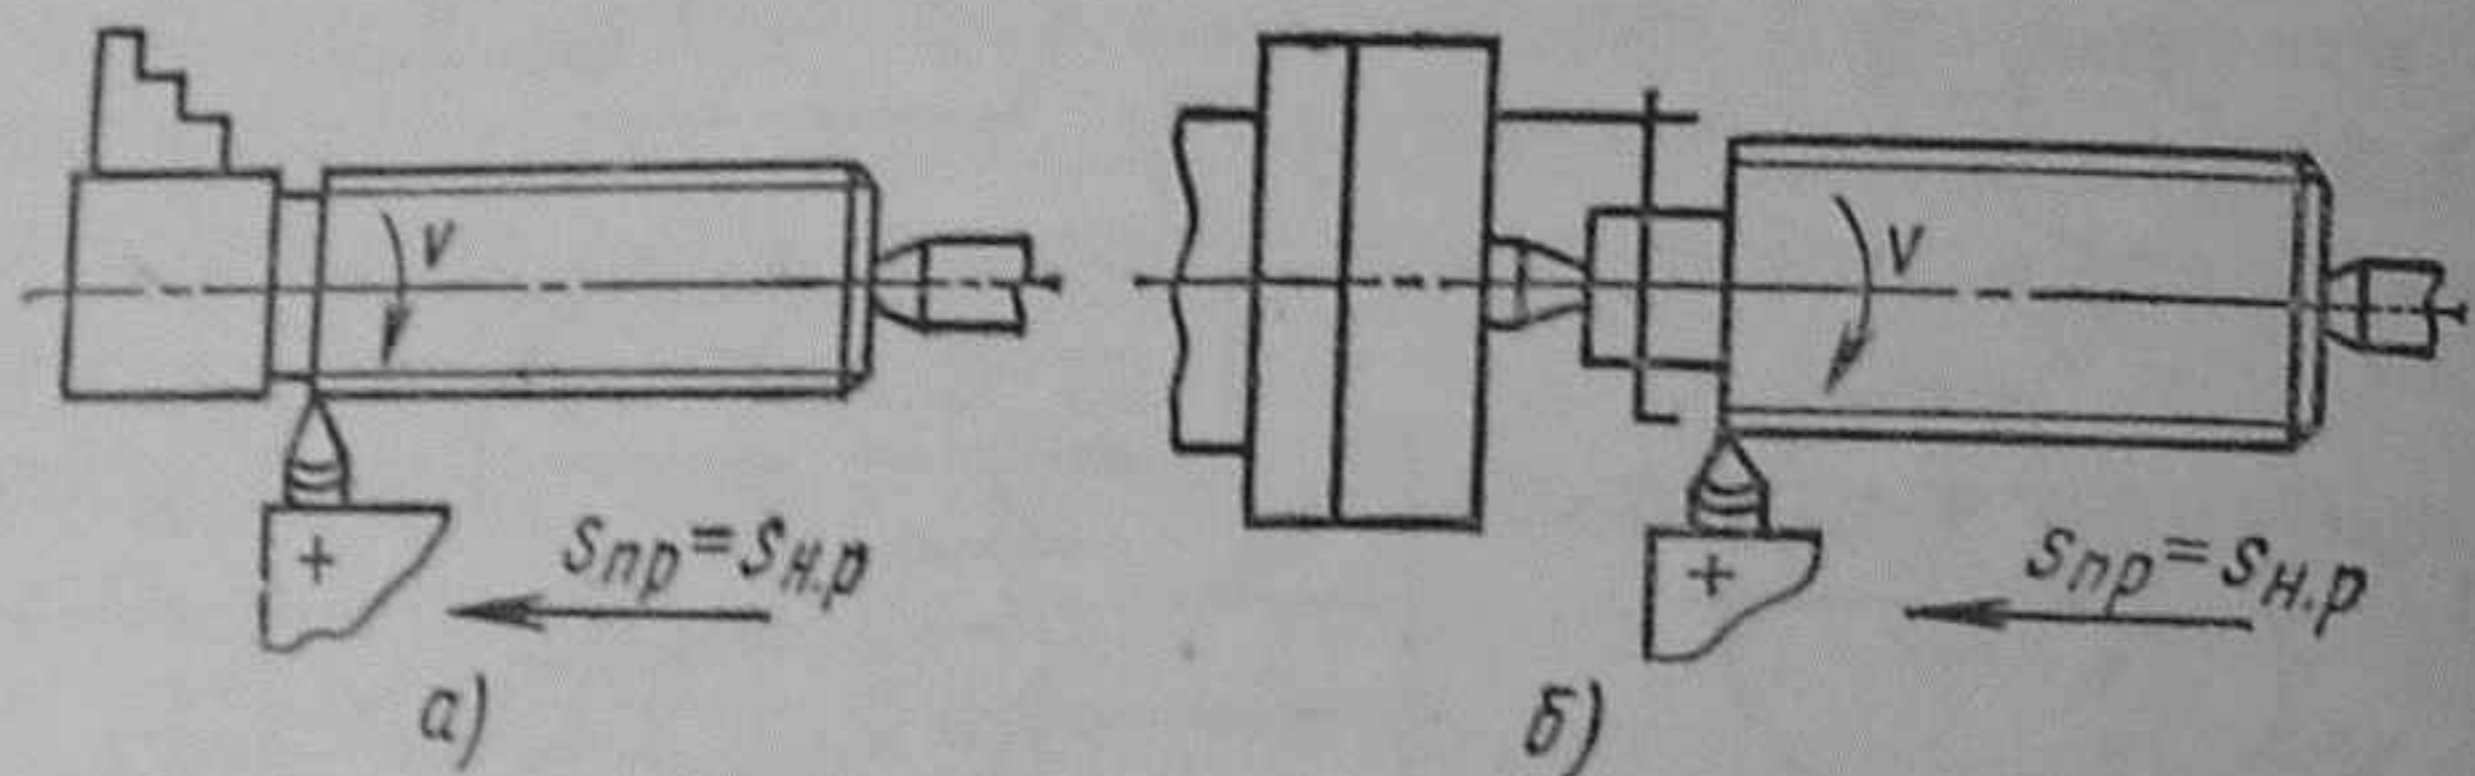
Схемы нарезания однозаходной и многозаходной резьбы на токарно-винторезном станке
